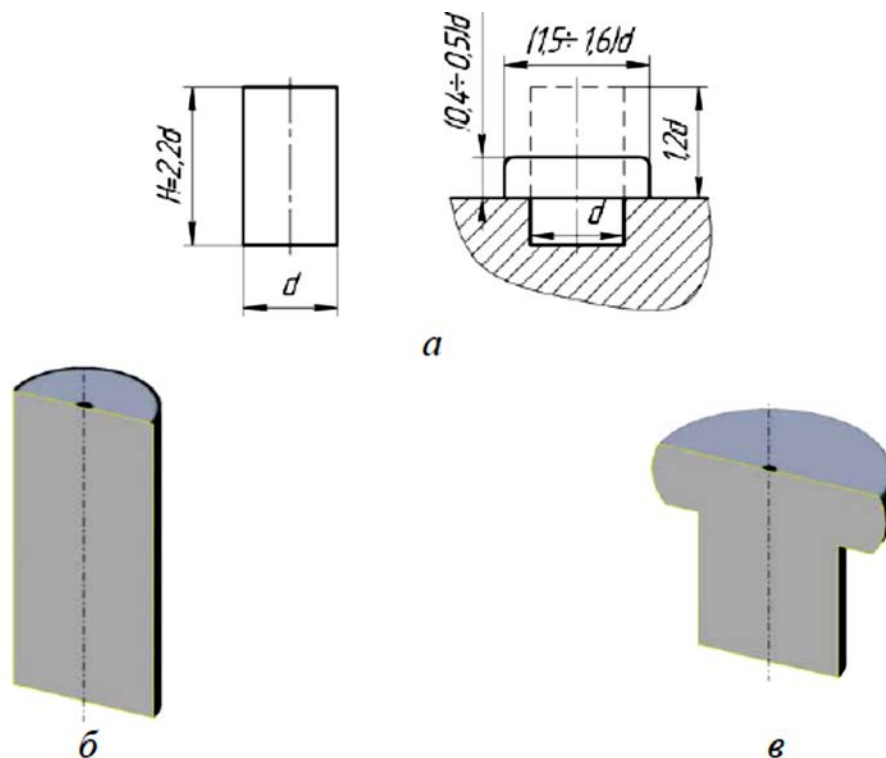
Проба на расплющивание: а – схема испытания; б – образец до испытания; в – образец после испытания
